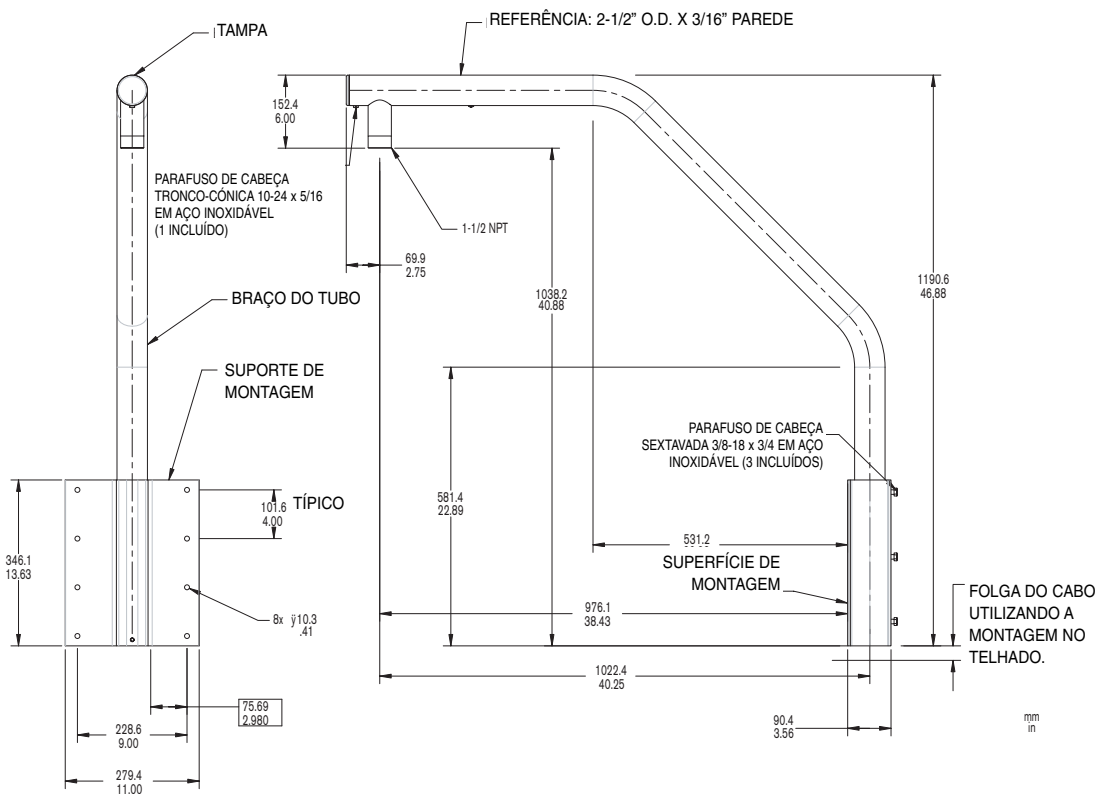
LTC 9230/00 Montagem no telhado (Parapeito)
